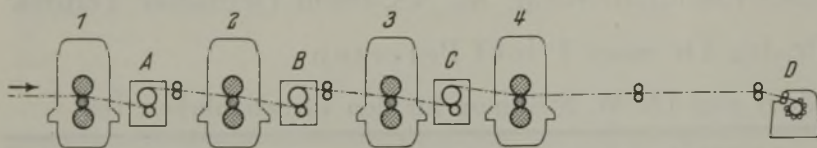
Vorschlag für ein Streifenwalzwerk nach E. Broemel mit hintereinanderstehenden Walzgerüsten und Haspelöfen.
